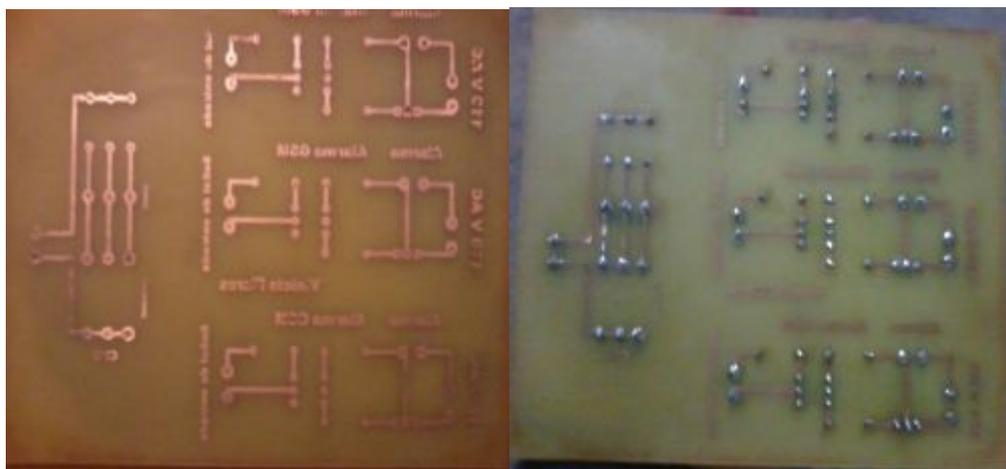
Diagrama de Cobre y Soldadura de Elementos.
